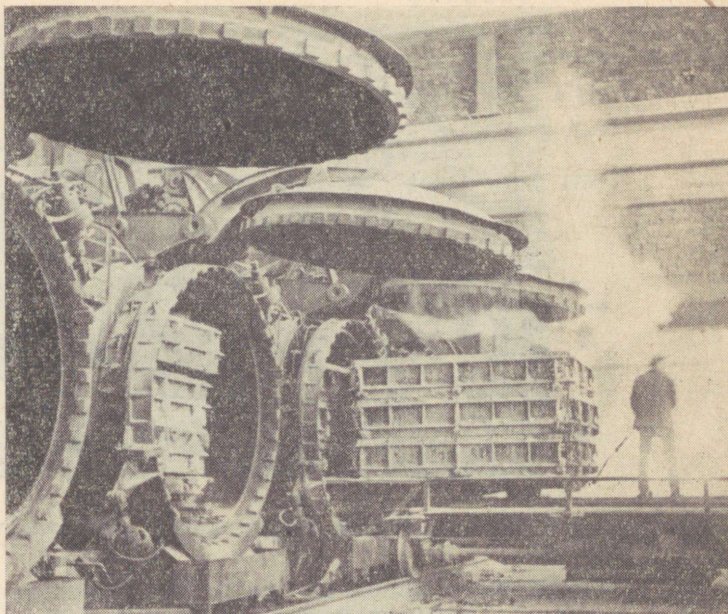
Выгрузка газокукермитовых деталей из автоклава.
